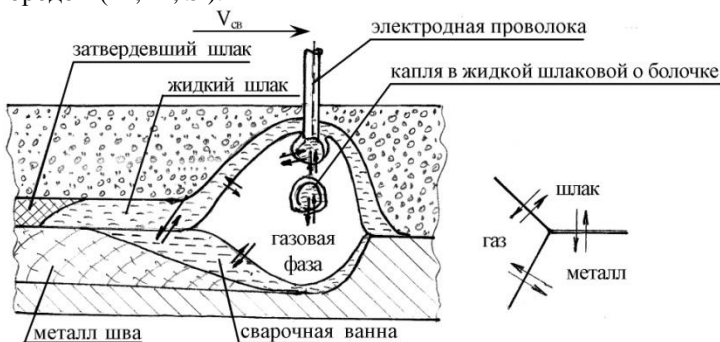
Схема взаимодействия металла сварочной ванны с газовой и шлаковой фазами.
